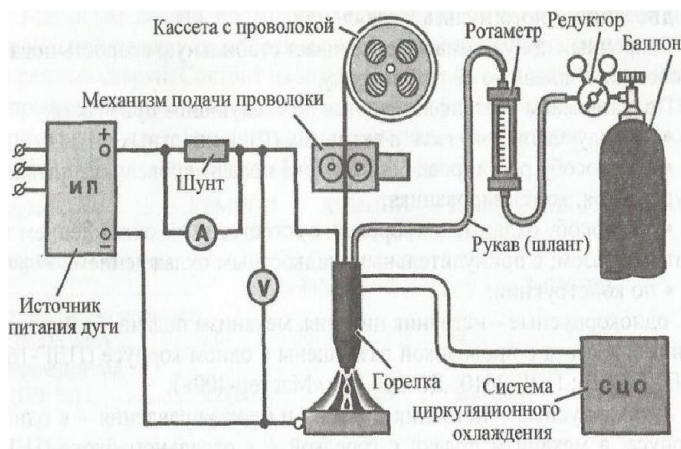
Комплект сварочного полуавтомата
